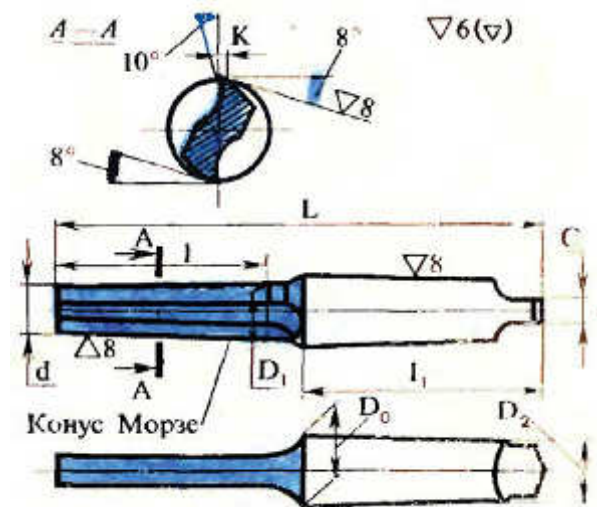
Двухперый конический зенкер для обработки стандартных конусов Морзе
